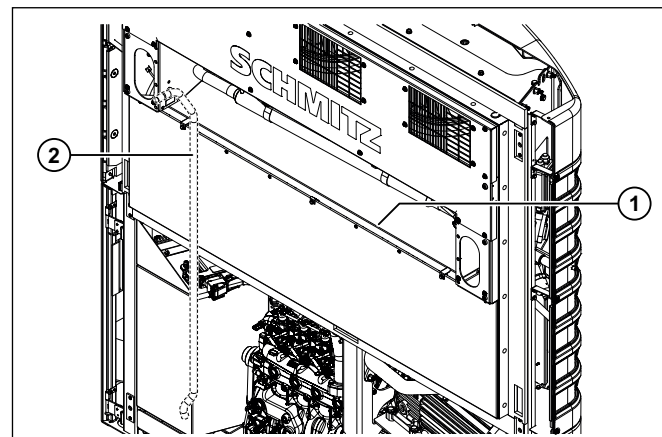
Contrôler la conduite d'évacuation de l'eau de dégivrage
